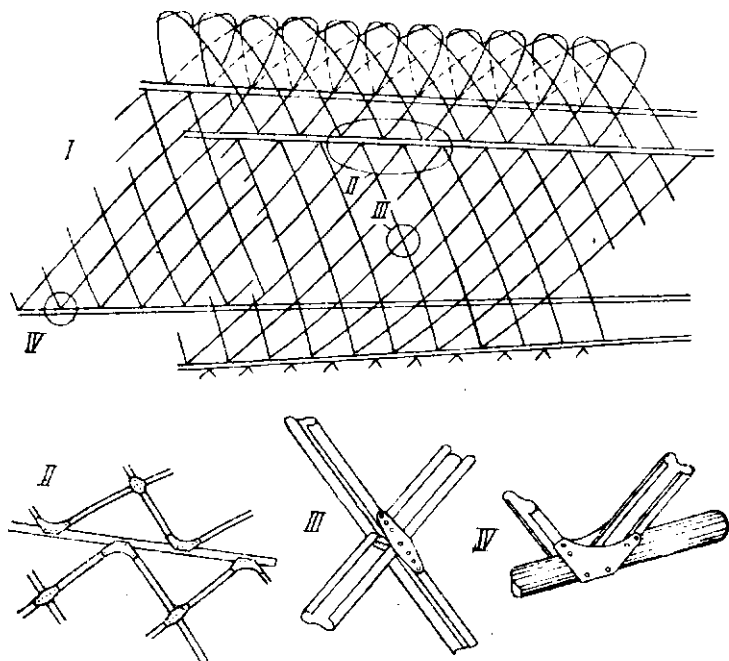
Схемы панелей раскосных ферменных фюзеляжей.
